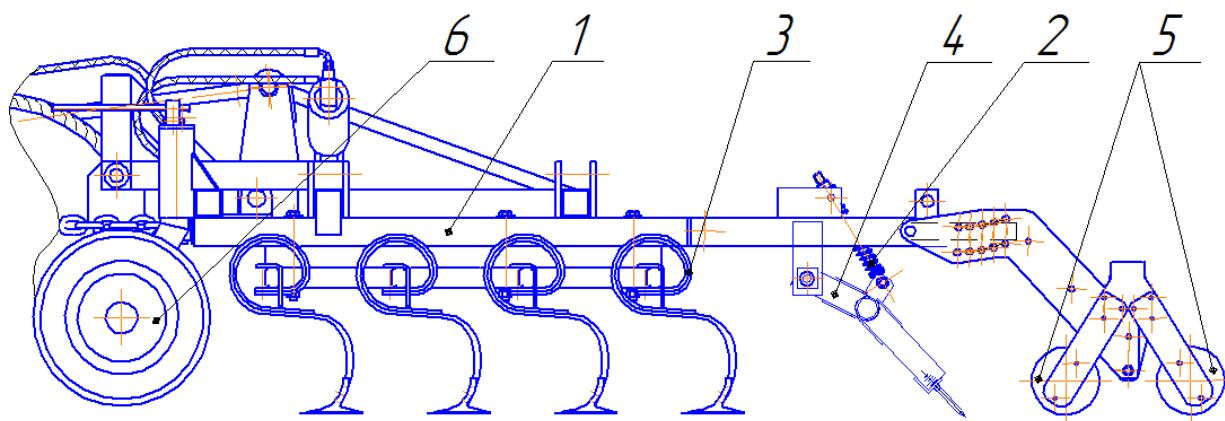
з Культиватор прицепной КБМ-10,8ПС-4Д.
